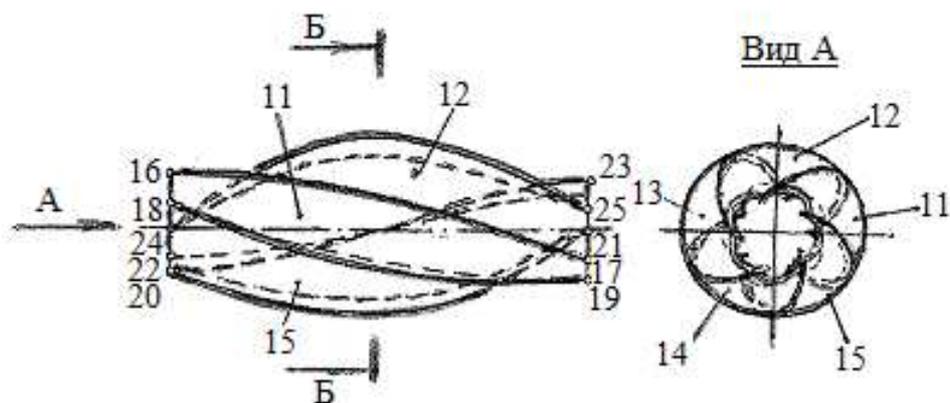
Релятивный винтовой бочкообразной формы станка для отделочно-зачистной и упрочняющей обработки деталей машин сельскохозяйственного назначения
